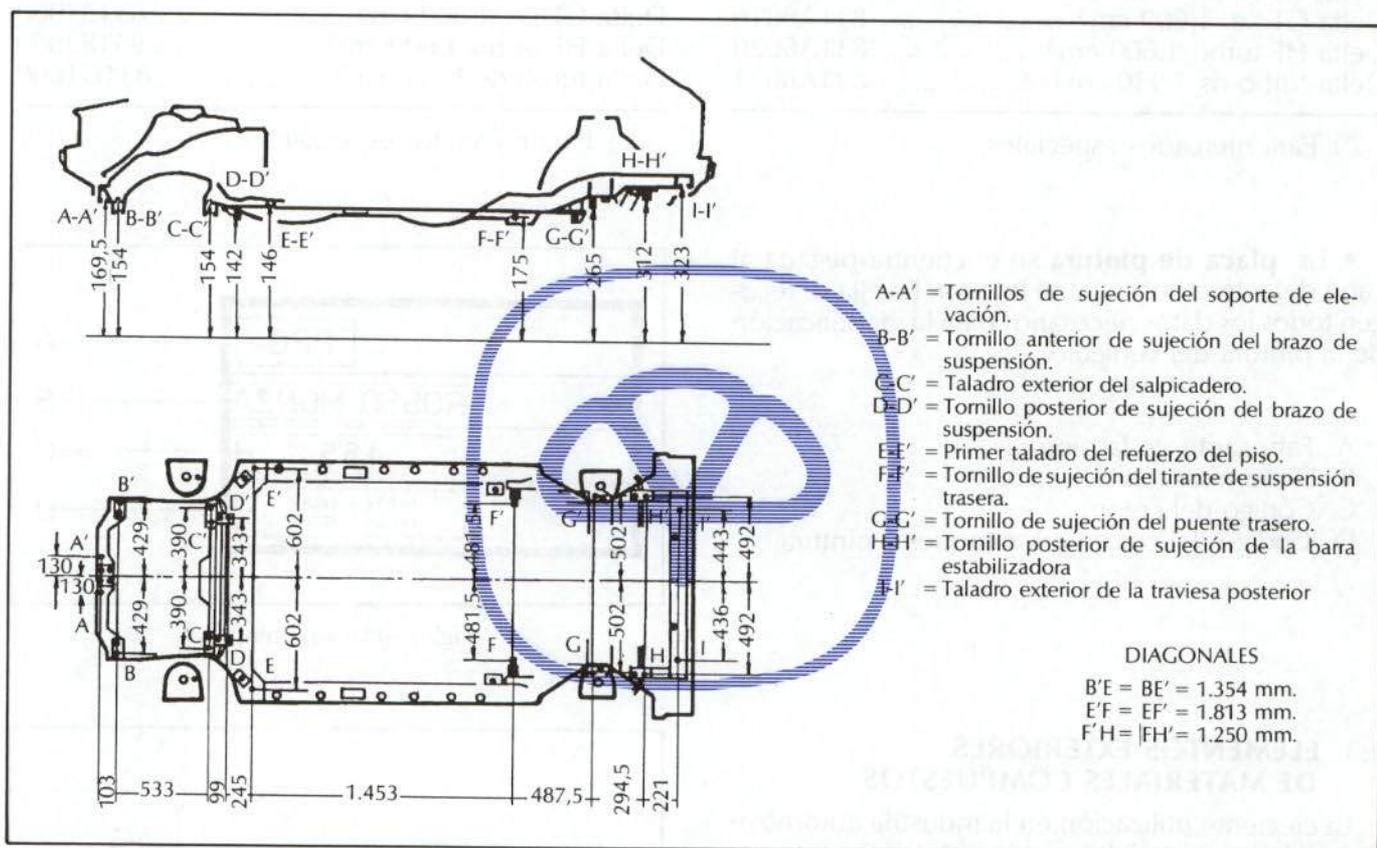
Dimensiones del vehículo en planta y alzado.
